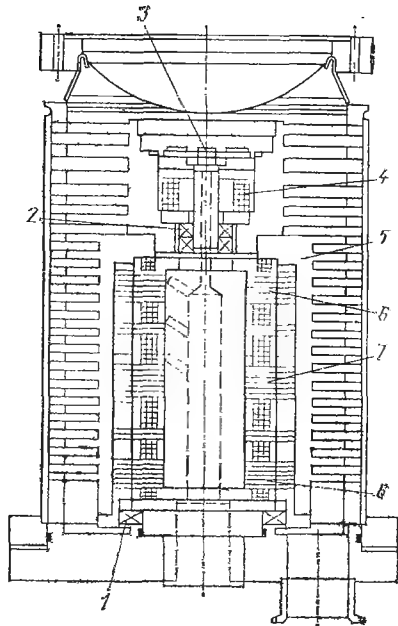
Конструктивная схема насоса «Турбовак-550М» с магнитной подвеской ротора
